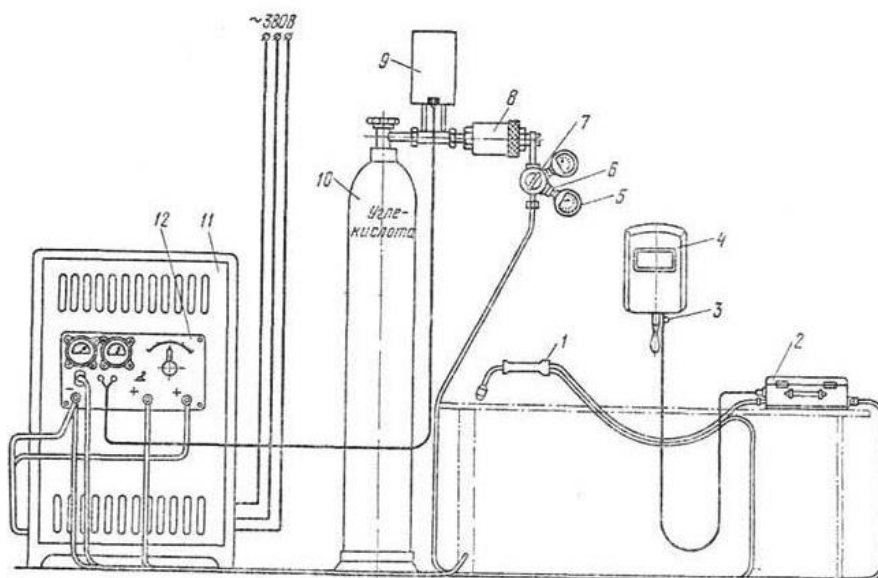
Схема поста полуавтоматической сварки тонкой электродной проволокой в углекислом газе: 1 — держатель; 2 — подающий механизм; 3 — кнопка включения; 4 — защитный щиток; 5 — манометр на 0,6 МПа; 6 — переходной штуцер для установки манометра; 7 — кислородный редуктор с манометром высокого давления; 8 — осушитель газа; 9 — подогреватель газа; 10 — баллон с углекислым газом; 11 — сварочный выпрямитель (или генератор); 12 — пульт управления.
